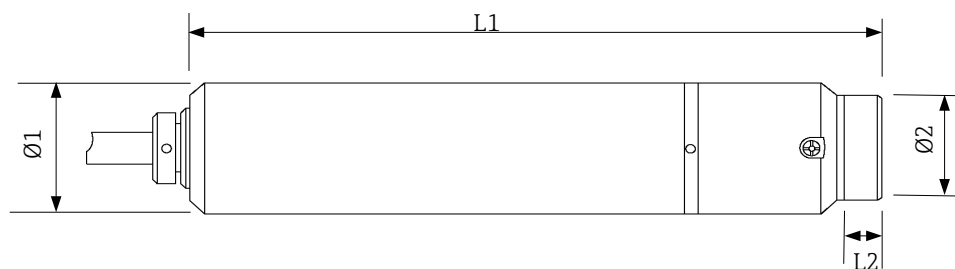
Dimensions de la sonde Rxn-20 et de l'adaptateur de lentille
